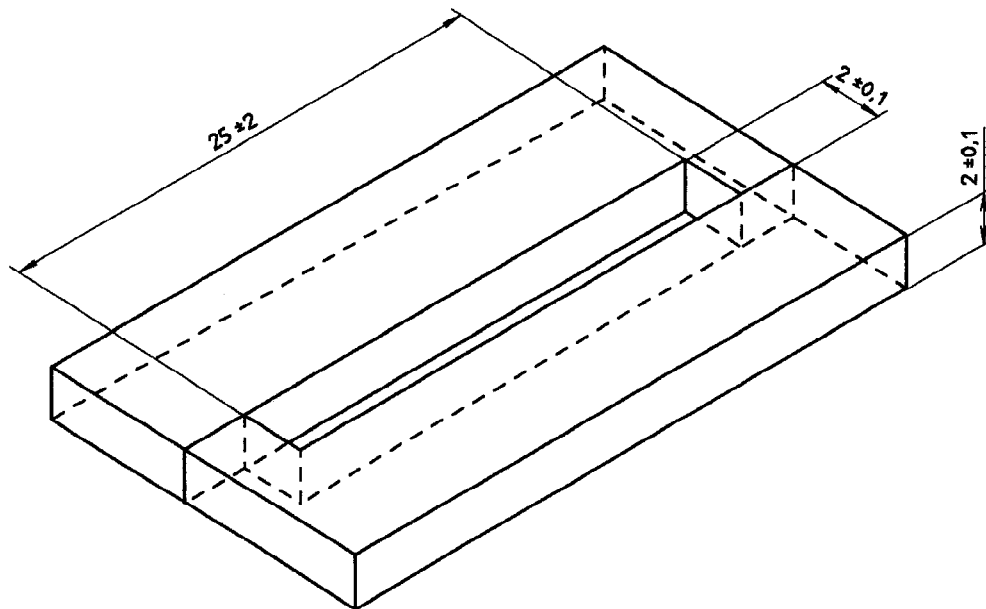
Moule fendu, en acier inoxydable, pour la préparation des éprouvettes pour essai de flexion
